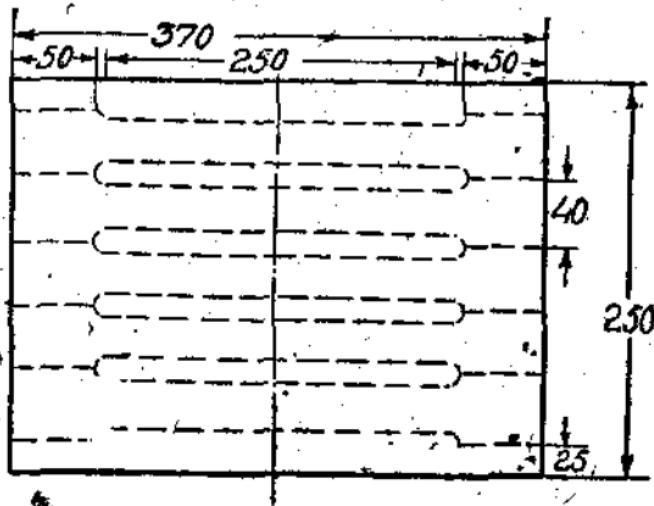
Изготовление образцов стыковой сварки.
